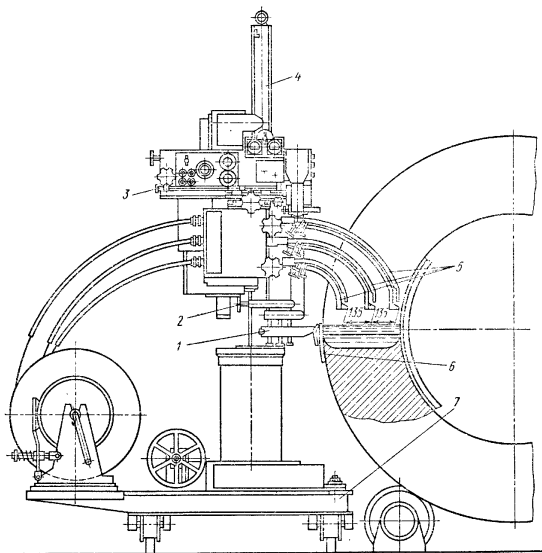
Установка для электрошлаковой сварки кольцевых швов с автоматом А535:
